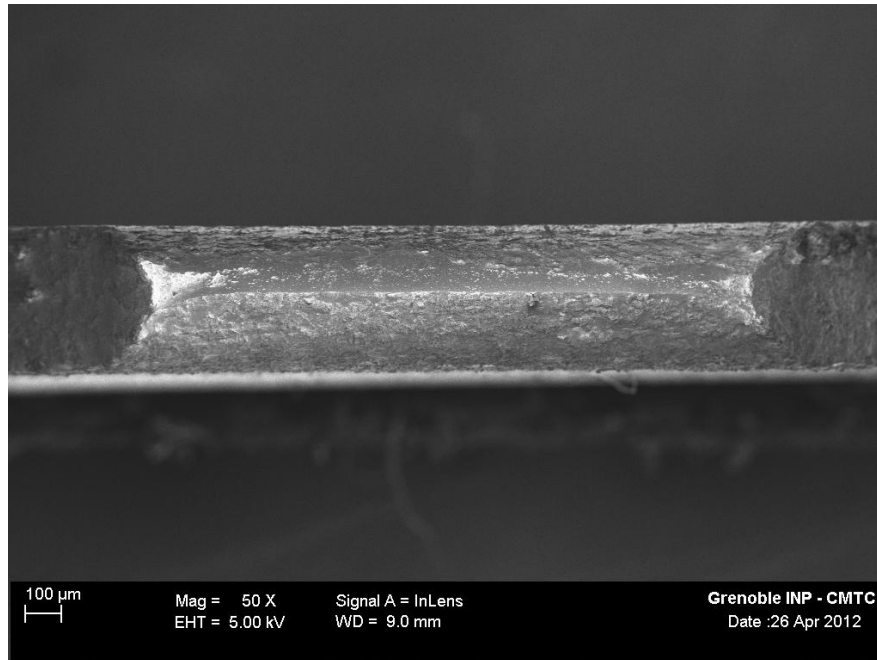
Fractografía de la probeta plana ASTM, con entalle en 90°, de cobre comercial 99,99%. Se muestra la zona de fractura que se localiza en el entalle.
